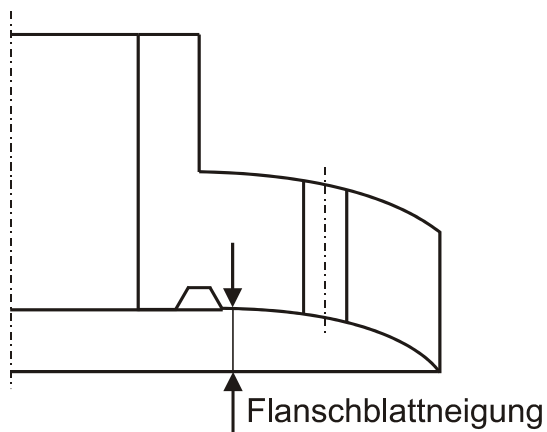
Messung der Flanschblattneigung bei Flansch A
